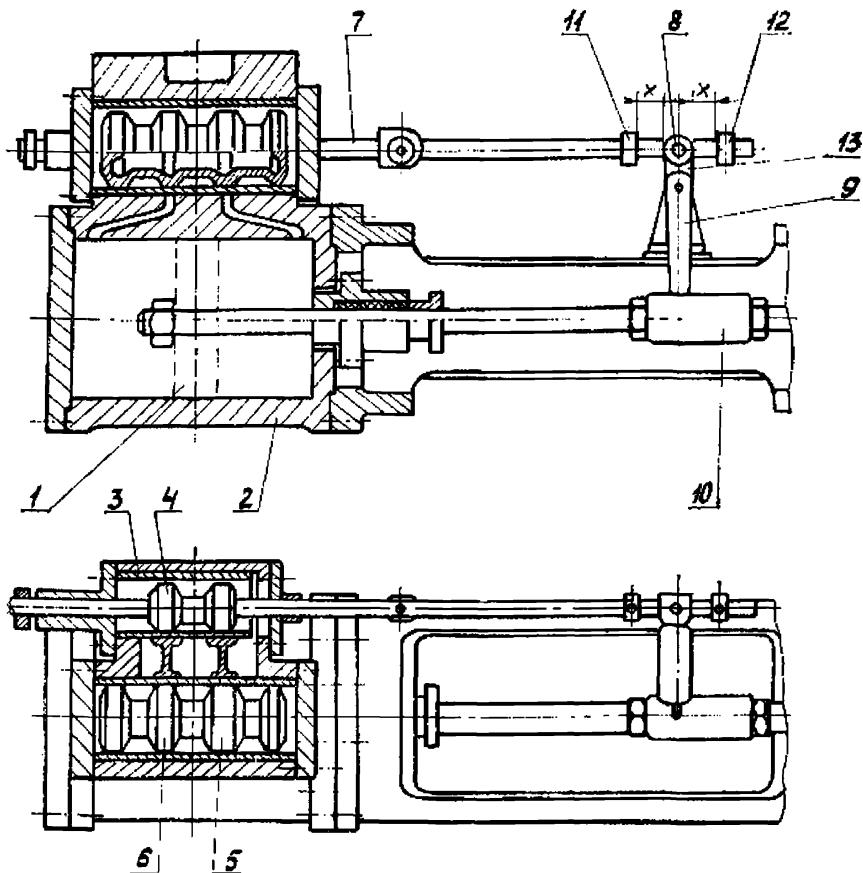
Паровой цилиндр и парораспределительный механизм насоса ПН:
